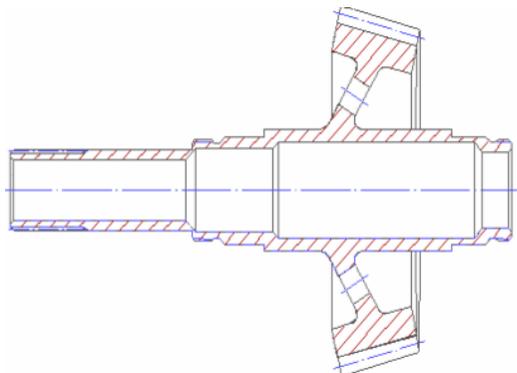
Конструкция вала-шестерни с внешним облегчением зубчатого колеса
